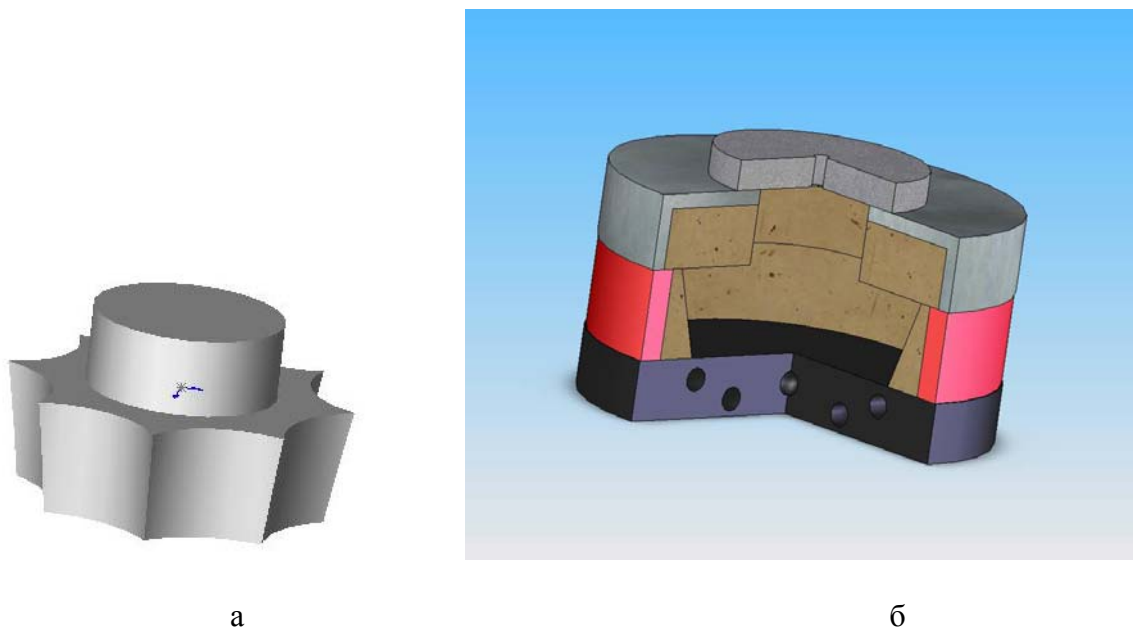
Зливоч нової форми (а) та конструкція виливниці (б) для його виготовлення
